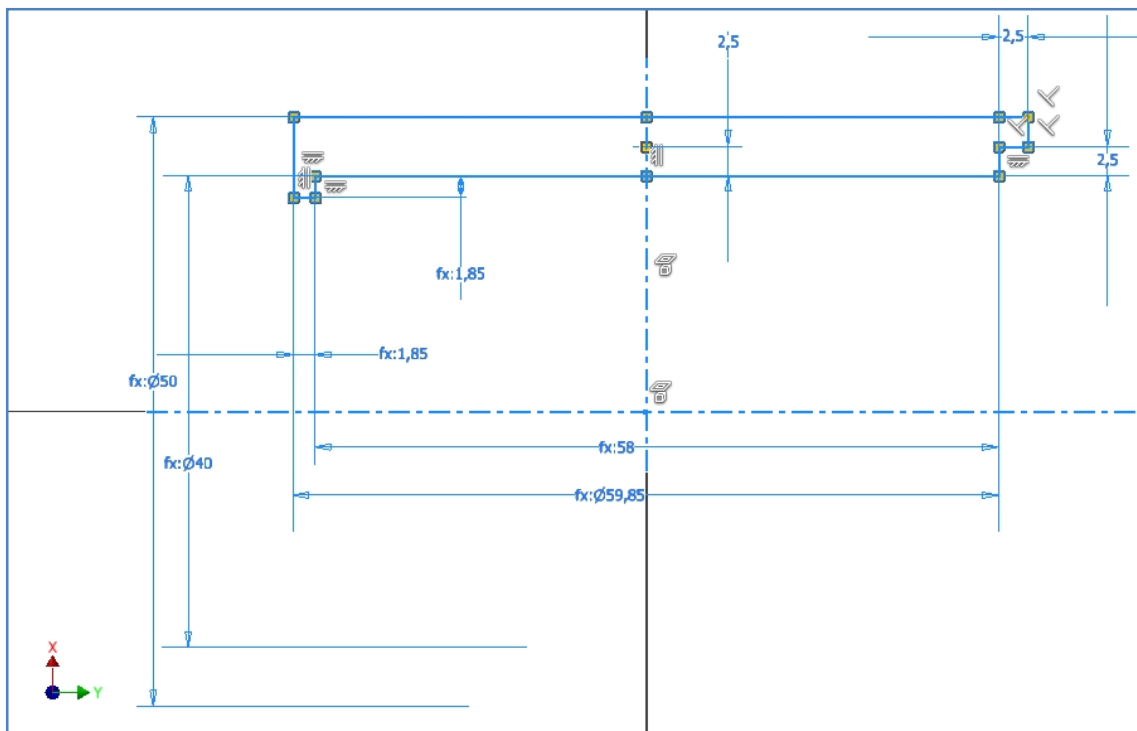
Primer boceto para la el soporte rodamiento lineal.
